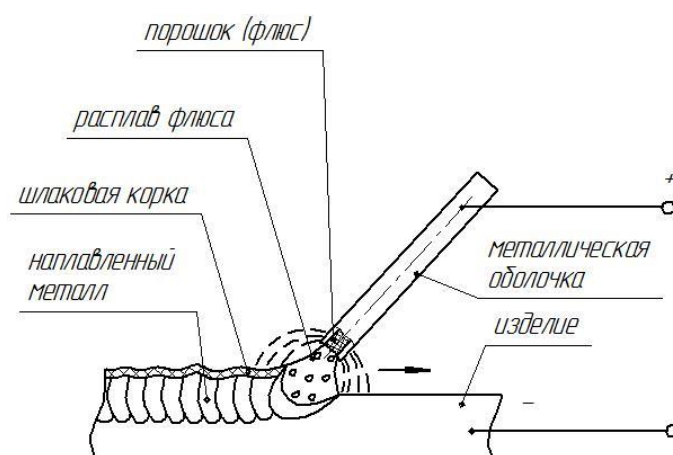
Схема осуществления сварки самозащитной порошковой проволокой
